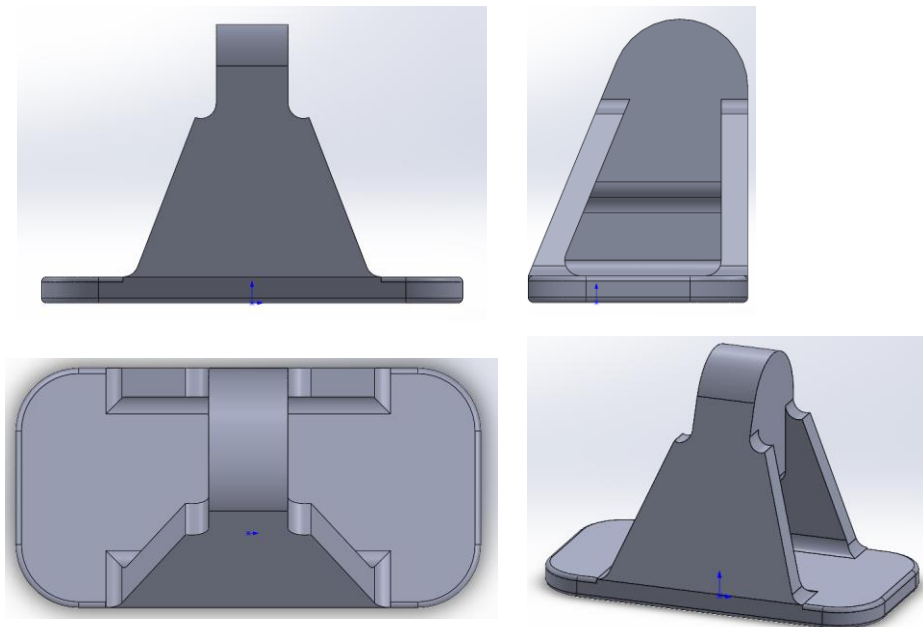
Комп'ютерна 3D–модель заготовки деталі «Кронштейн»
